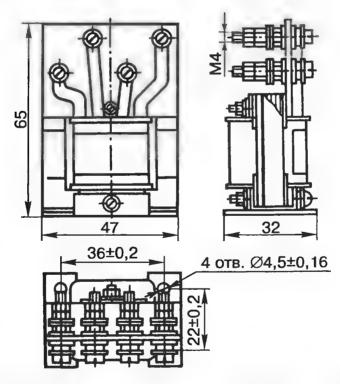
Присоединительные и габаритные размеры трансформатора РТ-3
